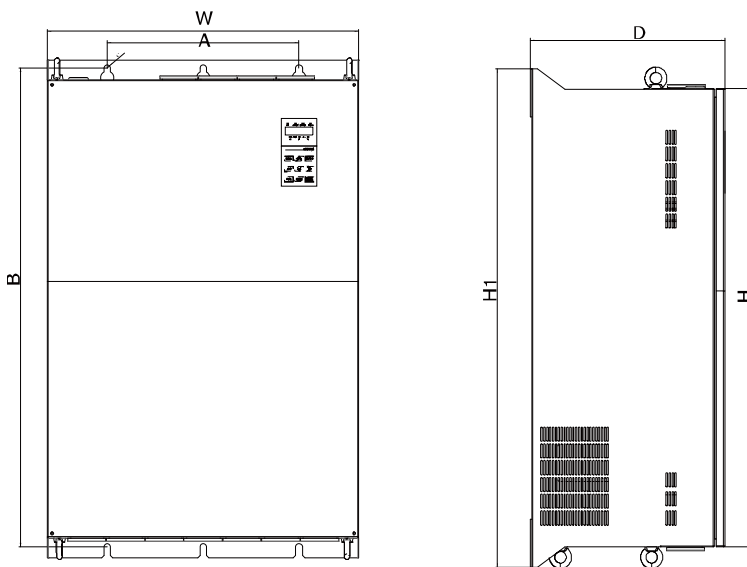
Схема внешних размеров и размеров монтажа металлической пластины ADL200G
